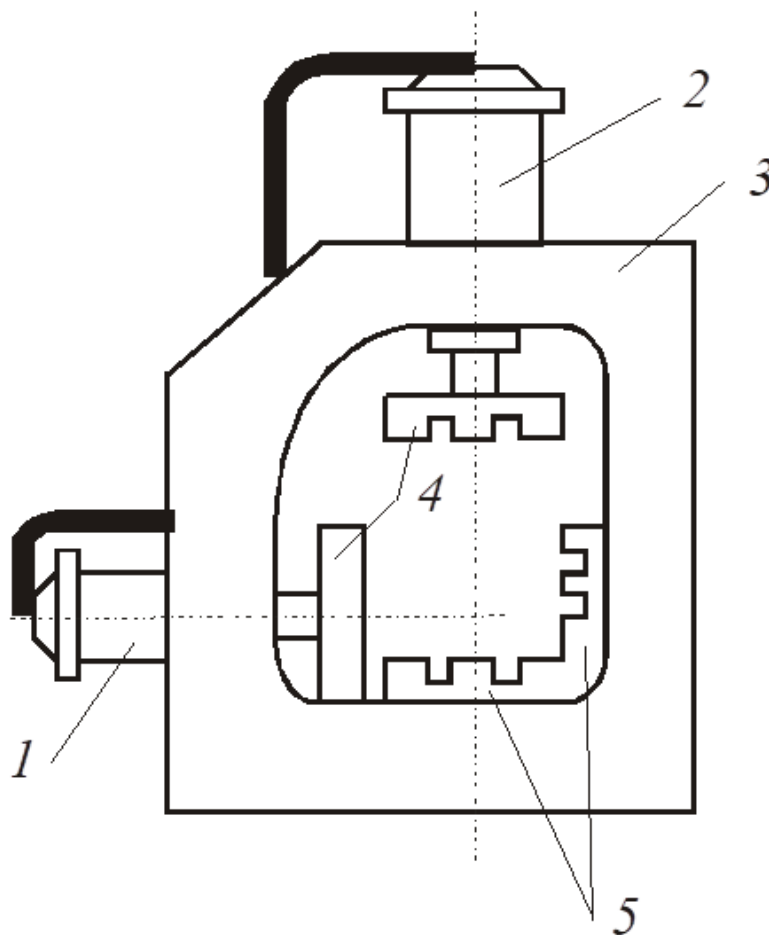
Угловой пресс с одним угловым цилиндром: 1 – боковой гидроцилиндр; 2 – верхний гидроцилиндр; 3 – рама (стойка); 4 – подвижные рабочие плиты; 5 – неподвижные рабочие плиты
